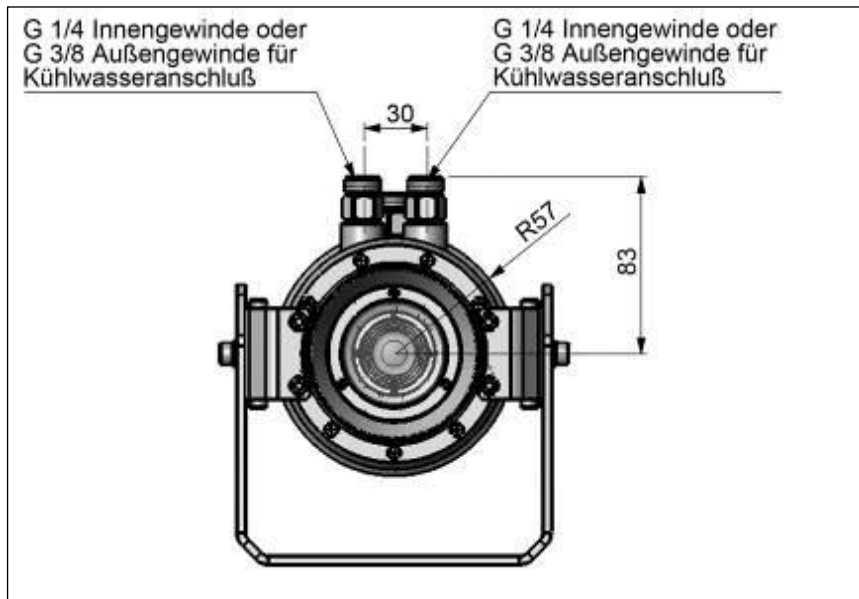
CoolingJacket Advanced, Standard-Version – Komplettansicht
